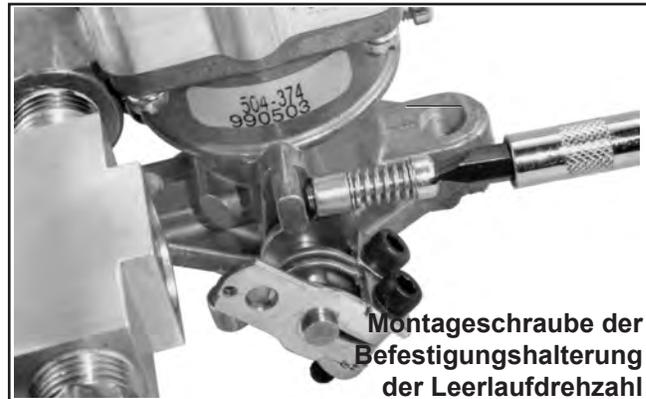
A-8. Die Leerlaufschraube abschrauben.
